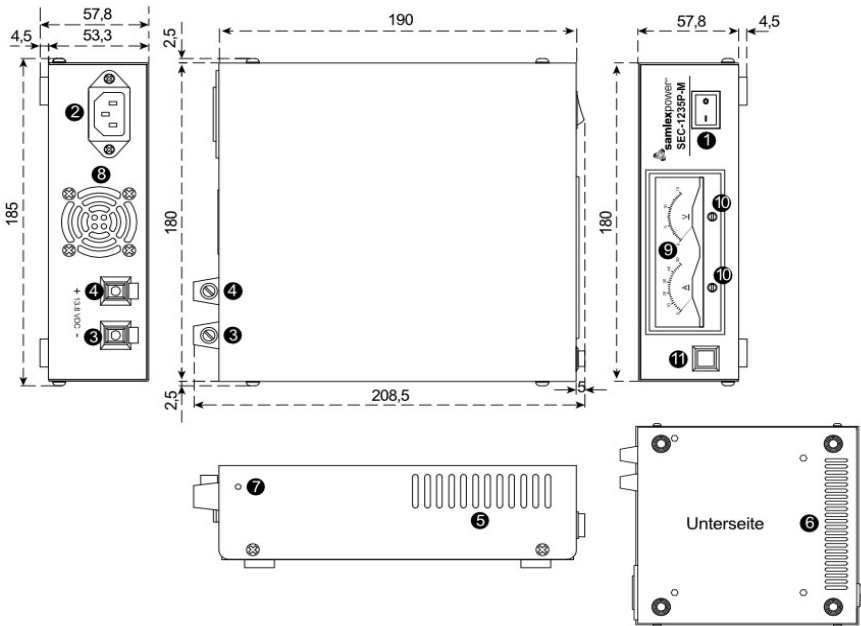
Layout & Abmessungen - SEC-1235P-M
